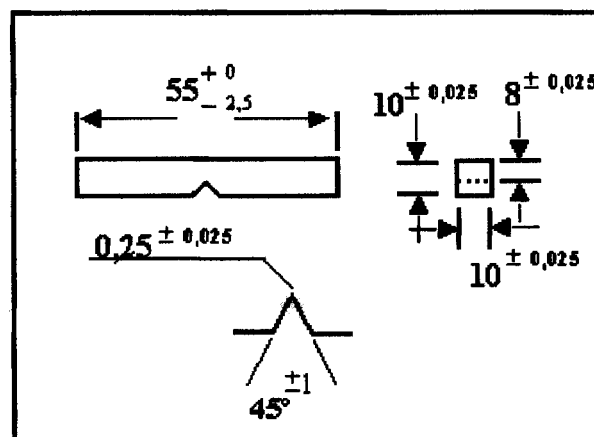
Dimensões dos corpos-de-prova para ensaio de impacto do tipo Charpy V, Norma ASTM E-23/89 (Dimensões em mm).
